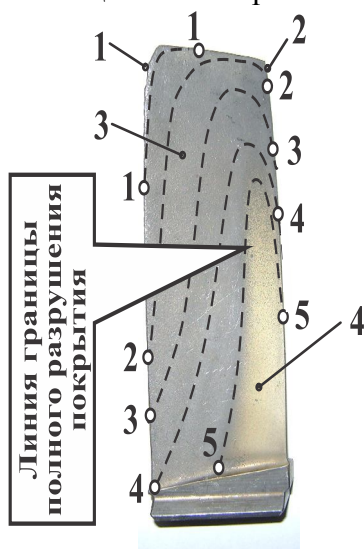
Схема неравномерного эрозионного разрушения (неравномерность 1-го рода) пера лопатки компрессора ГТД
